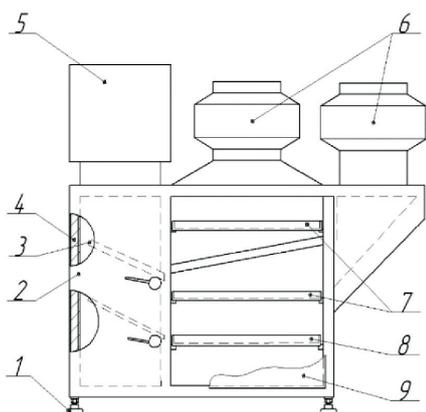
Охладитель гранул Ш12-РОГ: 1— опоры; 2 — корпус, 3 — заслонки, 4 — изоляция, 5 — электронагреватель; 6 — вентиляторы каналные; 7 — лотки с сетчатым дном для гранул, 8 — лоток для сбора масла, 9 — дверь
